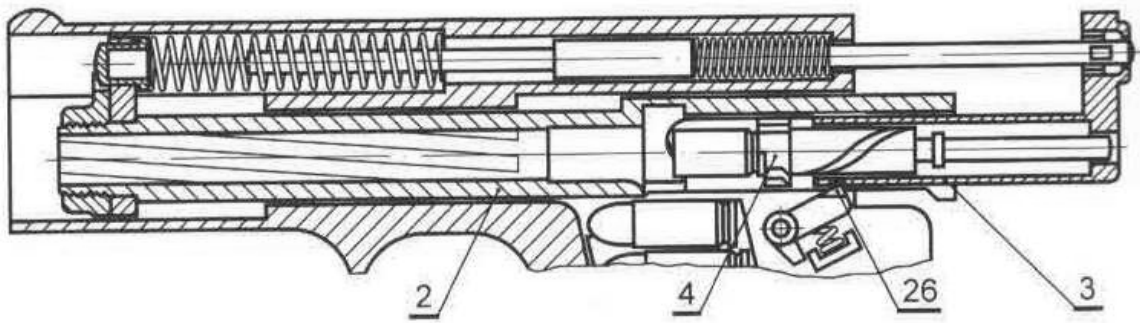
Samonabíjecí pistole Frommer Stop [12]
